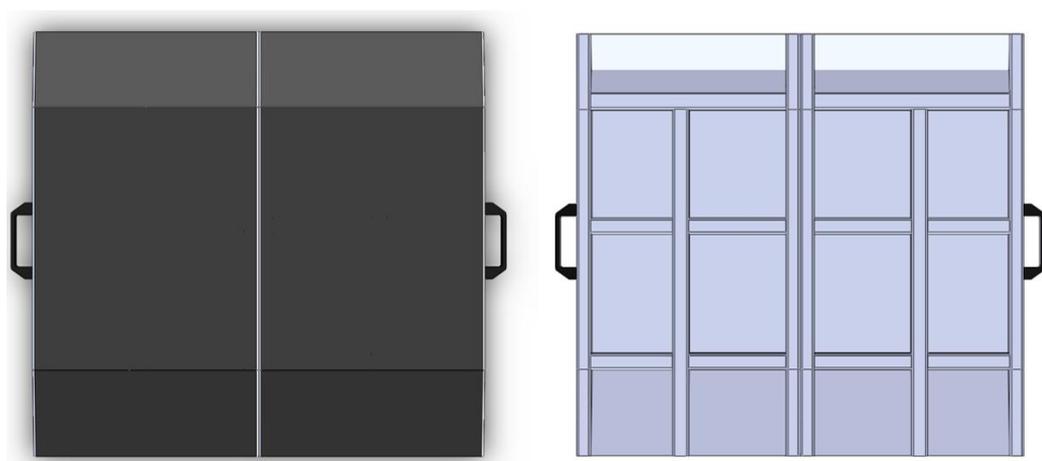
Vista Superior e Vista Inferior. Fonte: elaborado pelos autores.
